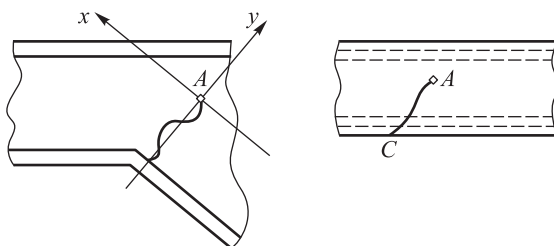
Схема контура концентратора напряжений в вершине трещины
